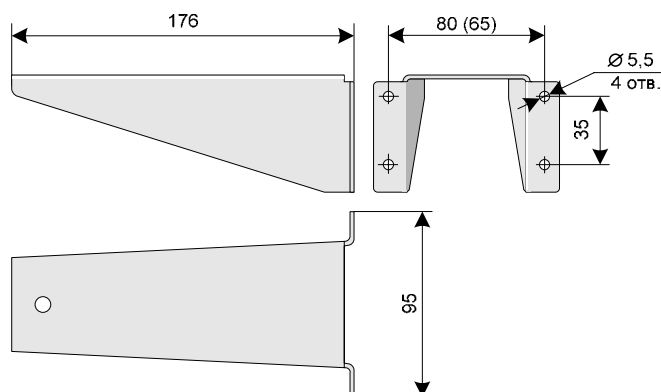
Кронштейн для крепления камеры в металлическом корпусе.
